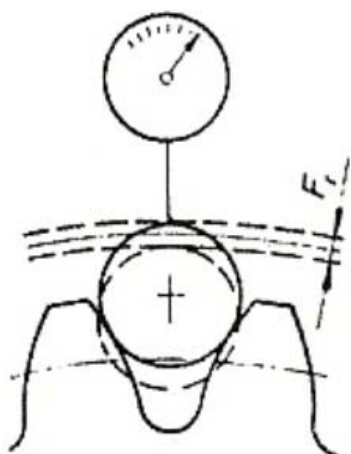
Místa kontroly házení ozubených kol po soustružení [8]
